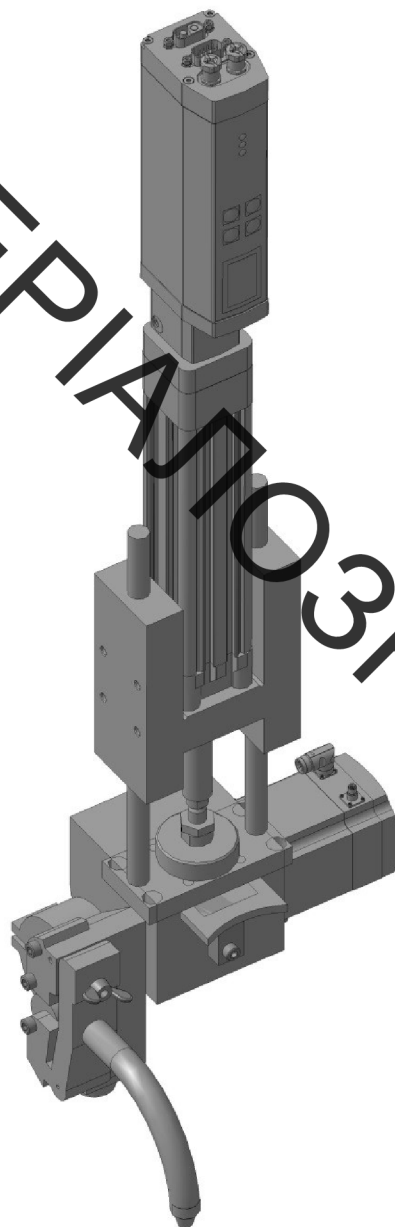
Консольний привід в зборі з наплавлювальною головкою.
